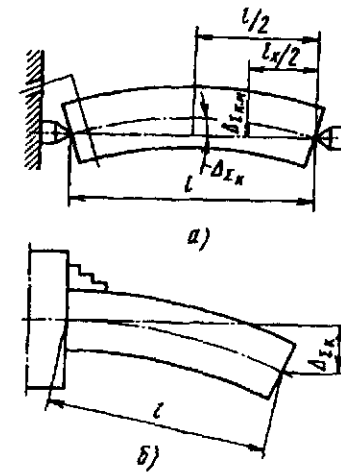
Обозначения общей и местной кривизны заготовки: а – при ее установке в центрах; б – при консольном креплении
